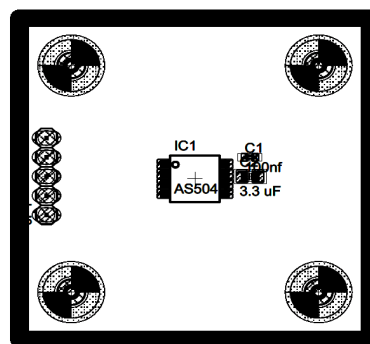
Návrh desky plošných spojů v poměru 2:1
